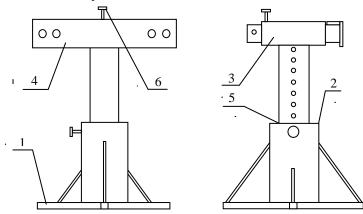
Стойка кантователя несущего кузова легкового автомобиля: a — вид спереди; б — вид сбоку; 1 — основание; 2 — направляющая стойка; 3 — регулировочная опора; 4 — поворотная планка; 5 — фиксатор регулировочной опоры; 6 — фиксатор поворотной планки
